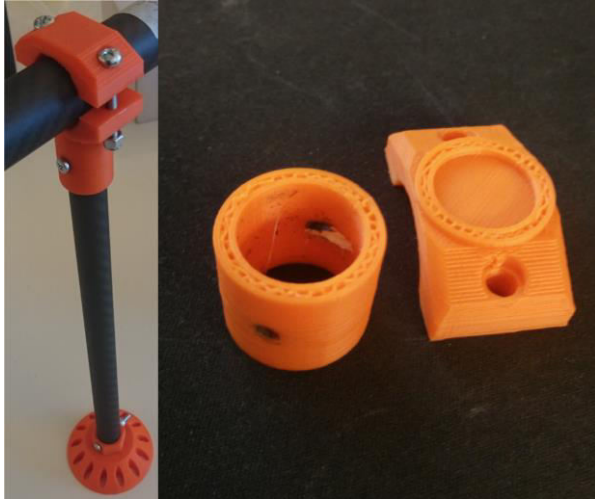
Till vänster: Motorblock V2. Mitten: Motorblock efter krasch. till höger: Motorblock V3[64].
